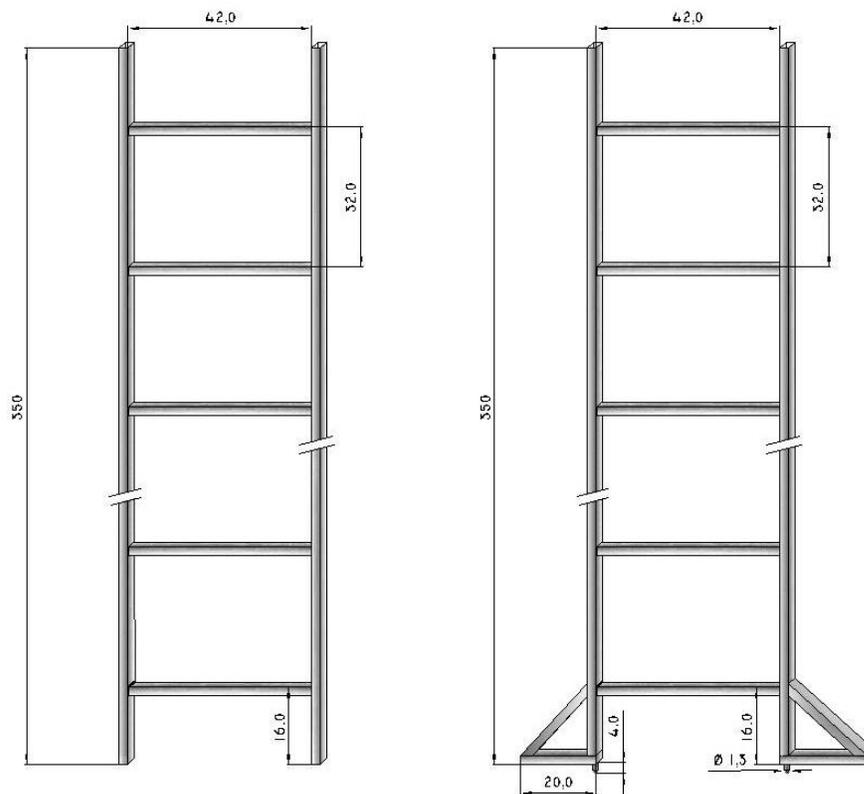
Desenho técnico da escada convencional (A) e modificada (B). Dimensões em cm
